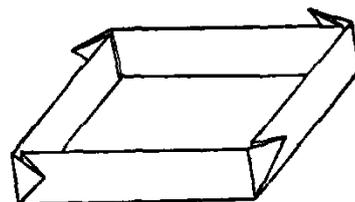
/2. Durch Hohlraumbildung schwimmfähig gemachte Blechscheibe
